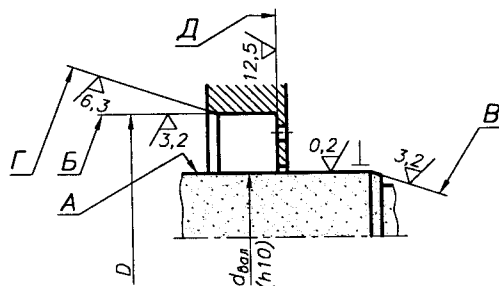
Шероховатость поверхностей установки манжеты
